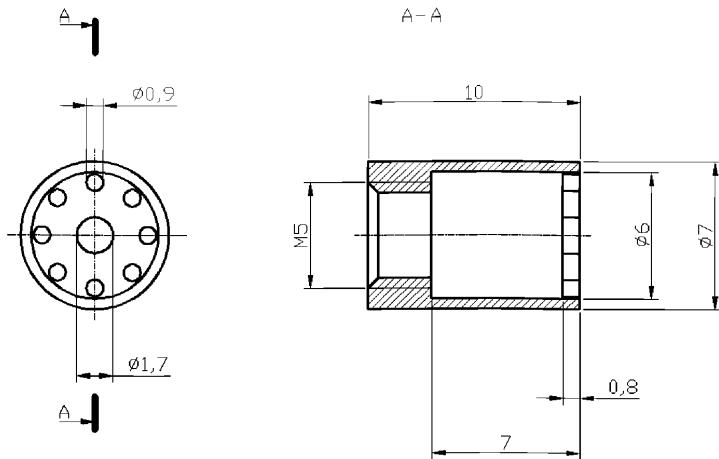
Горелка для зажигания образца (стабилизатор пламени горелки)
